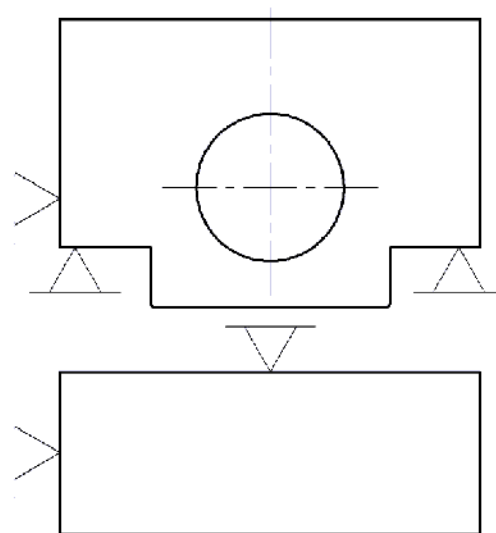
Схема установки заготовки на тактовому столі
